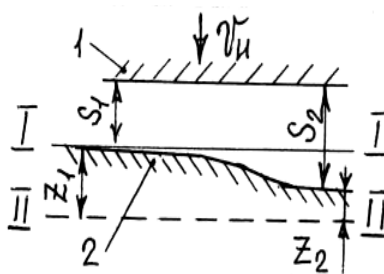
Схема до розрахунку припуску на обробку: 1 – електрод-інструмент; 2 – заготовка
